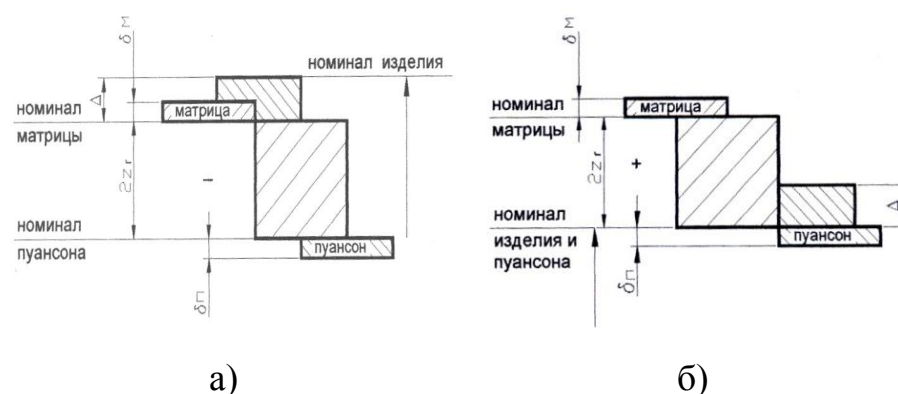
Схема расположения полей допусков на исполнительные размеры матрицы и пуансона при вытяжке детали «чашка» для двух возможных случаев сопряжения деталей – по наружному (а) и по внутреннему (б) контуру.
